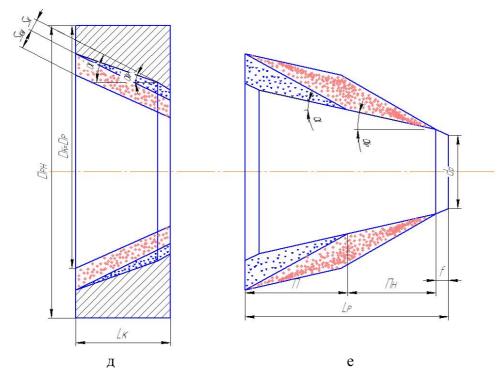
Схема сопряжения рабочих конических поверхностей ротора и корпуса установки Камюр
